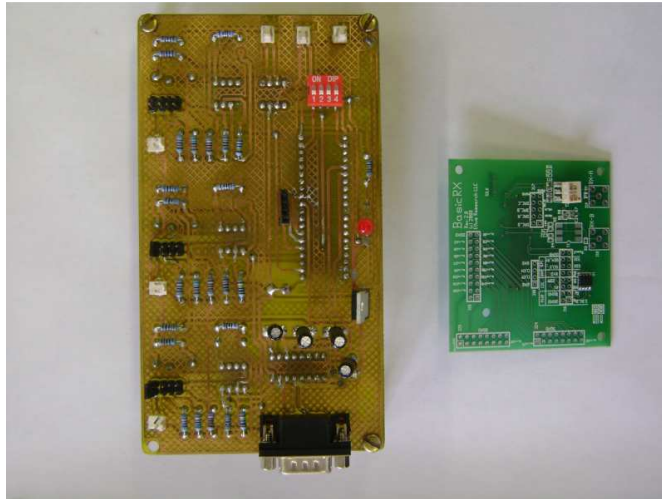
Comparação entre uma placa PCB comum e a placa SMD soldada no LAPS.
